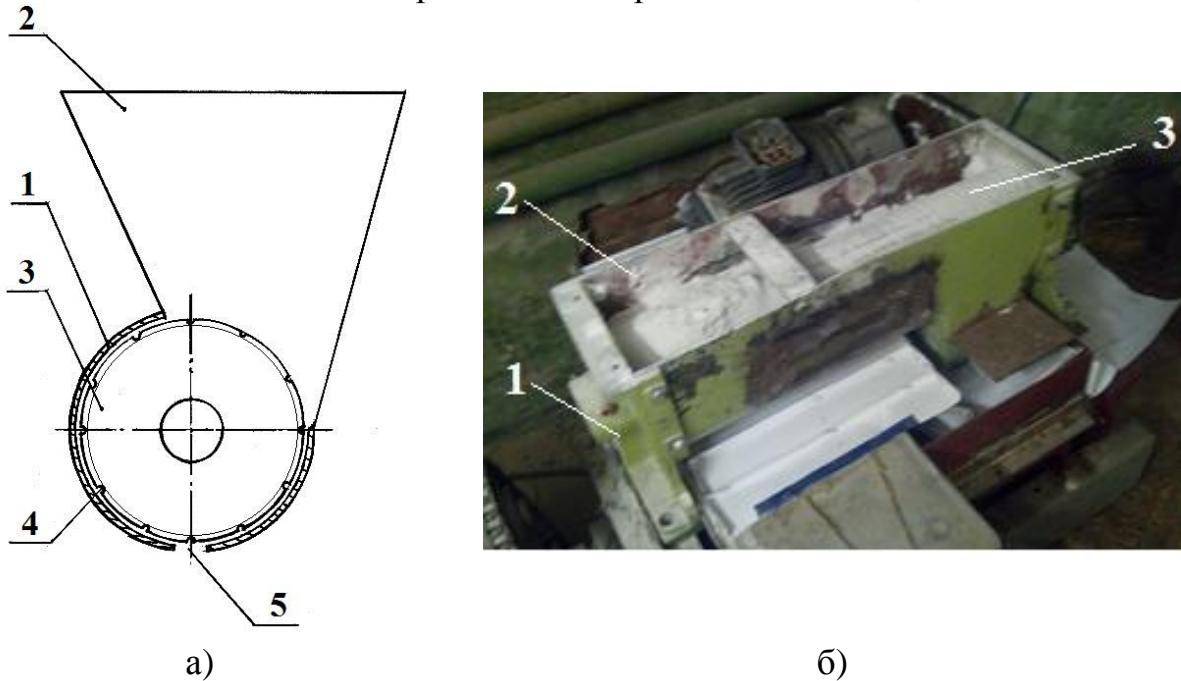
Дозатор для внесення пиловидного консерванту в силосну масу: а) конструктивно-технологічна схема; б) загальний вигляд; 1 – корпус; 2 – завантажувальний бункер; 3 – барабан; 4 – комірка напівсферичної форми; 5 – вивантажувальна щілина
